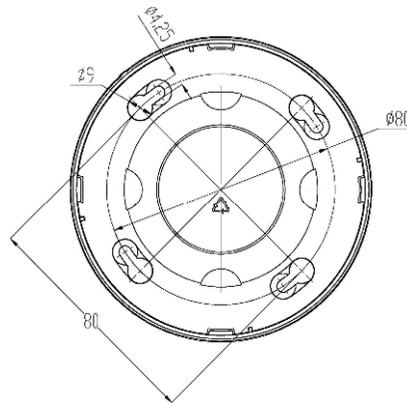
Расположение отверстий для крепления базы извещателя
